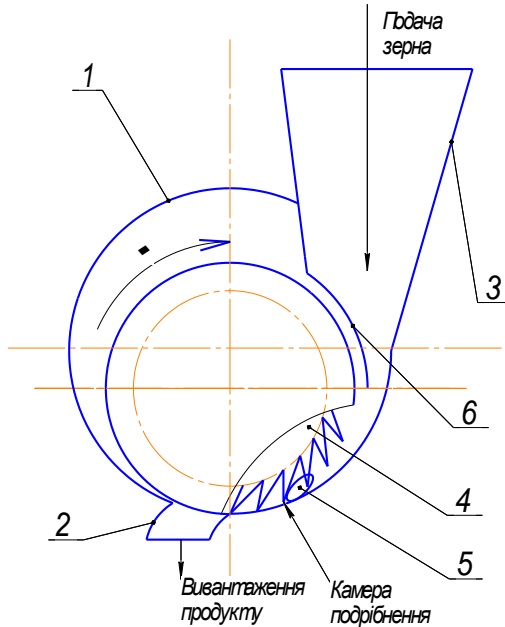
Конструктивно-технологічна схема подрібнювача зернових кормів: 1 - циліндричний корпус; 2 - вивантажувальний патрубок; 3 - бункер зерна; 4 - подрібнювальний ротор; 5 - зерно; 6 - обмежувальний кожух
